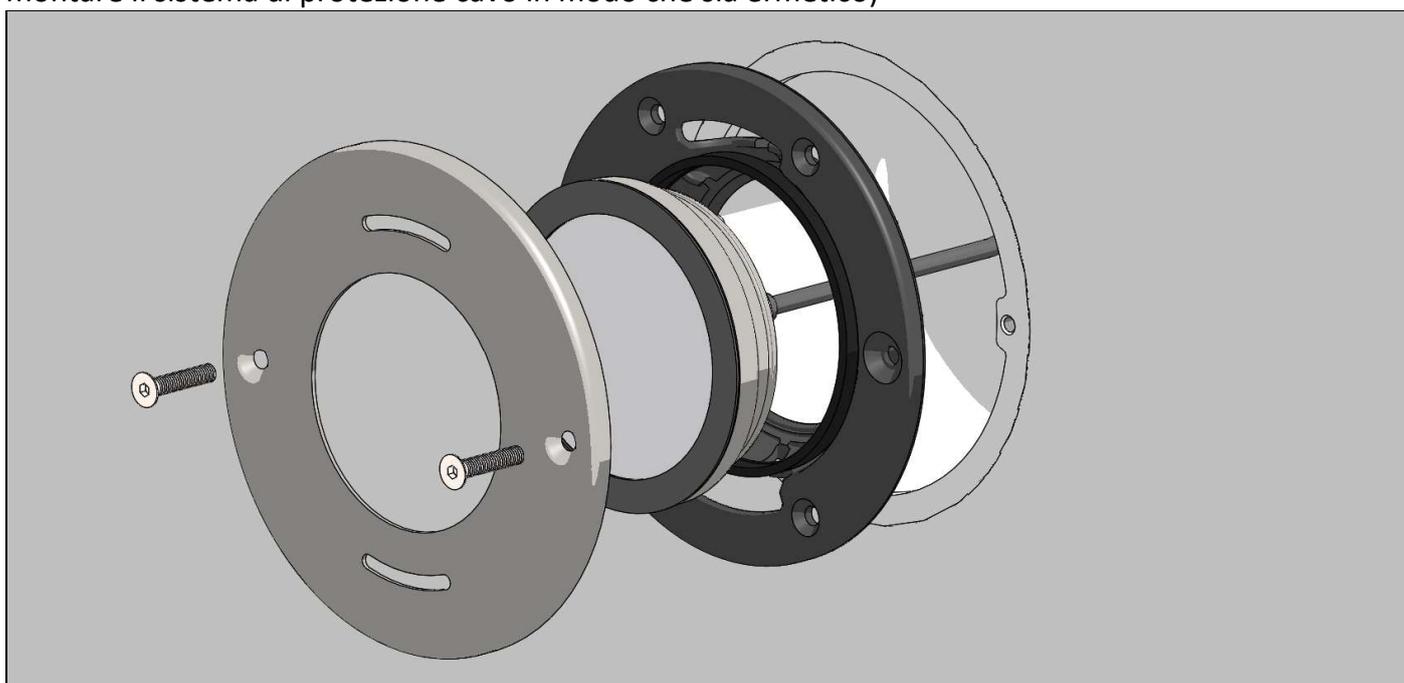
Kit di montaggio della piscina in acciaio (esempio con versione standard – rotonda)
